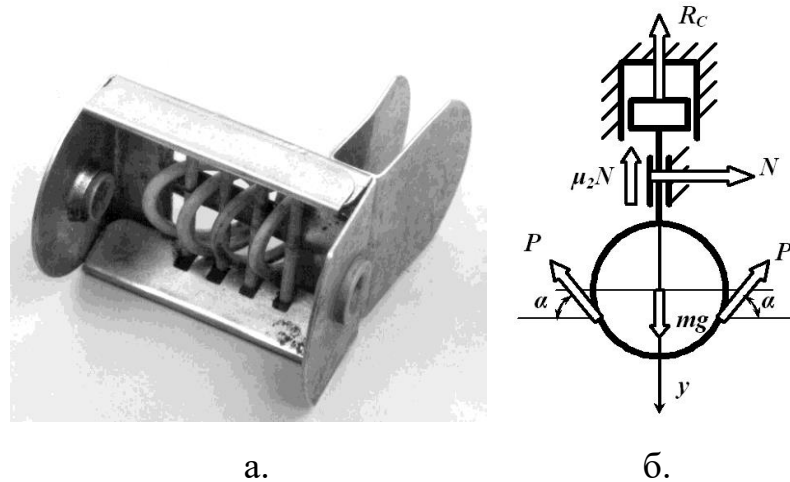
Загальний вигляд та розрахункова схема компенсатора натягу нитки з кільцями
